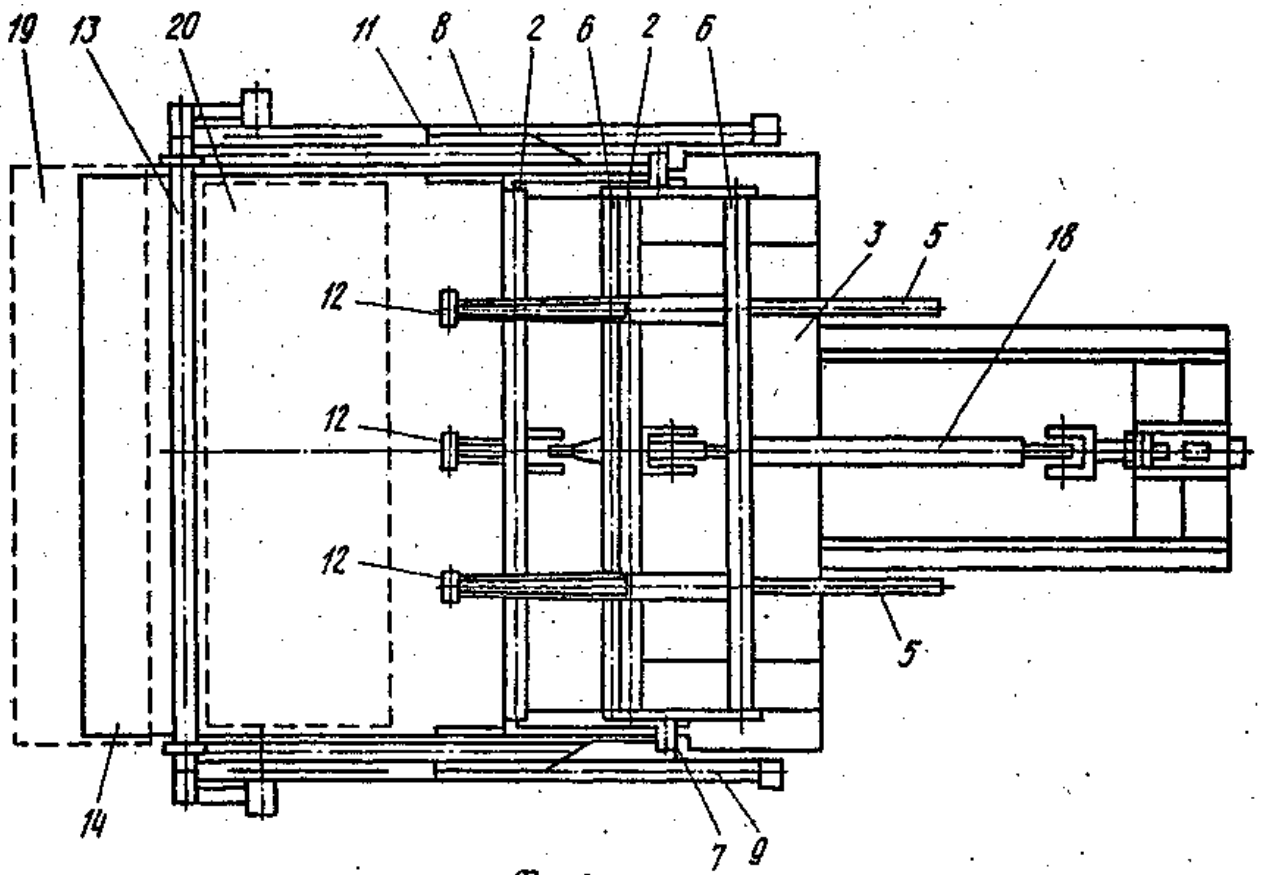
Загальний вигляд пристрою для закривання стулок коробів
